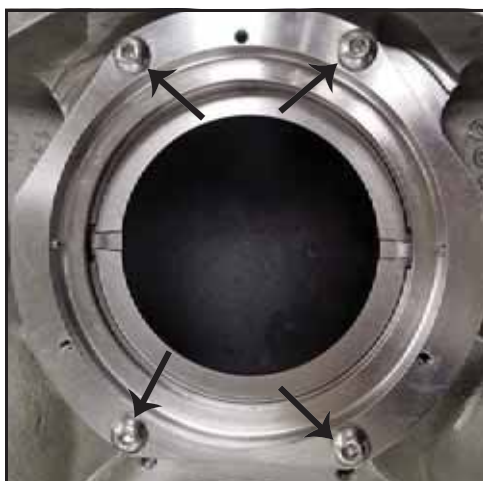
Założony pierścień o-ring obudowy uszczelnienia
